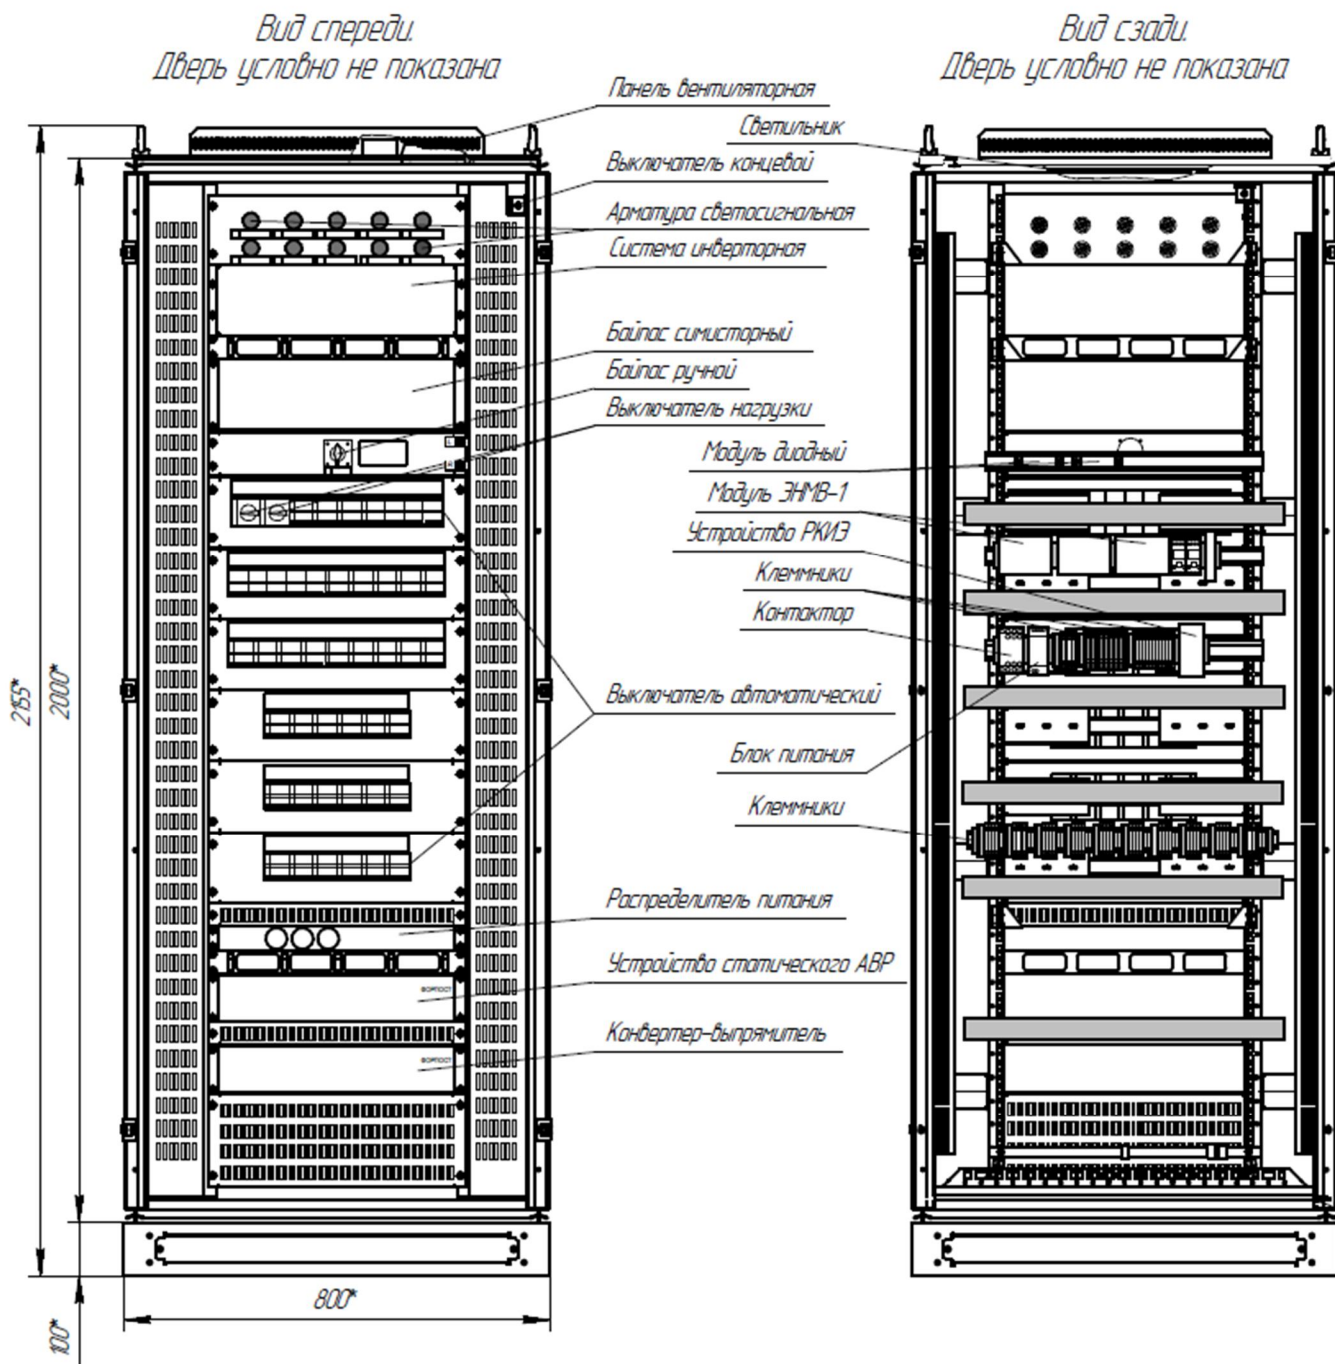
Общий вид и размеры шкафа № ЗНИ
